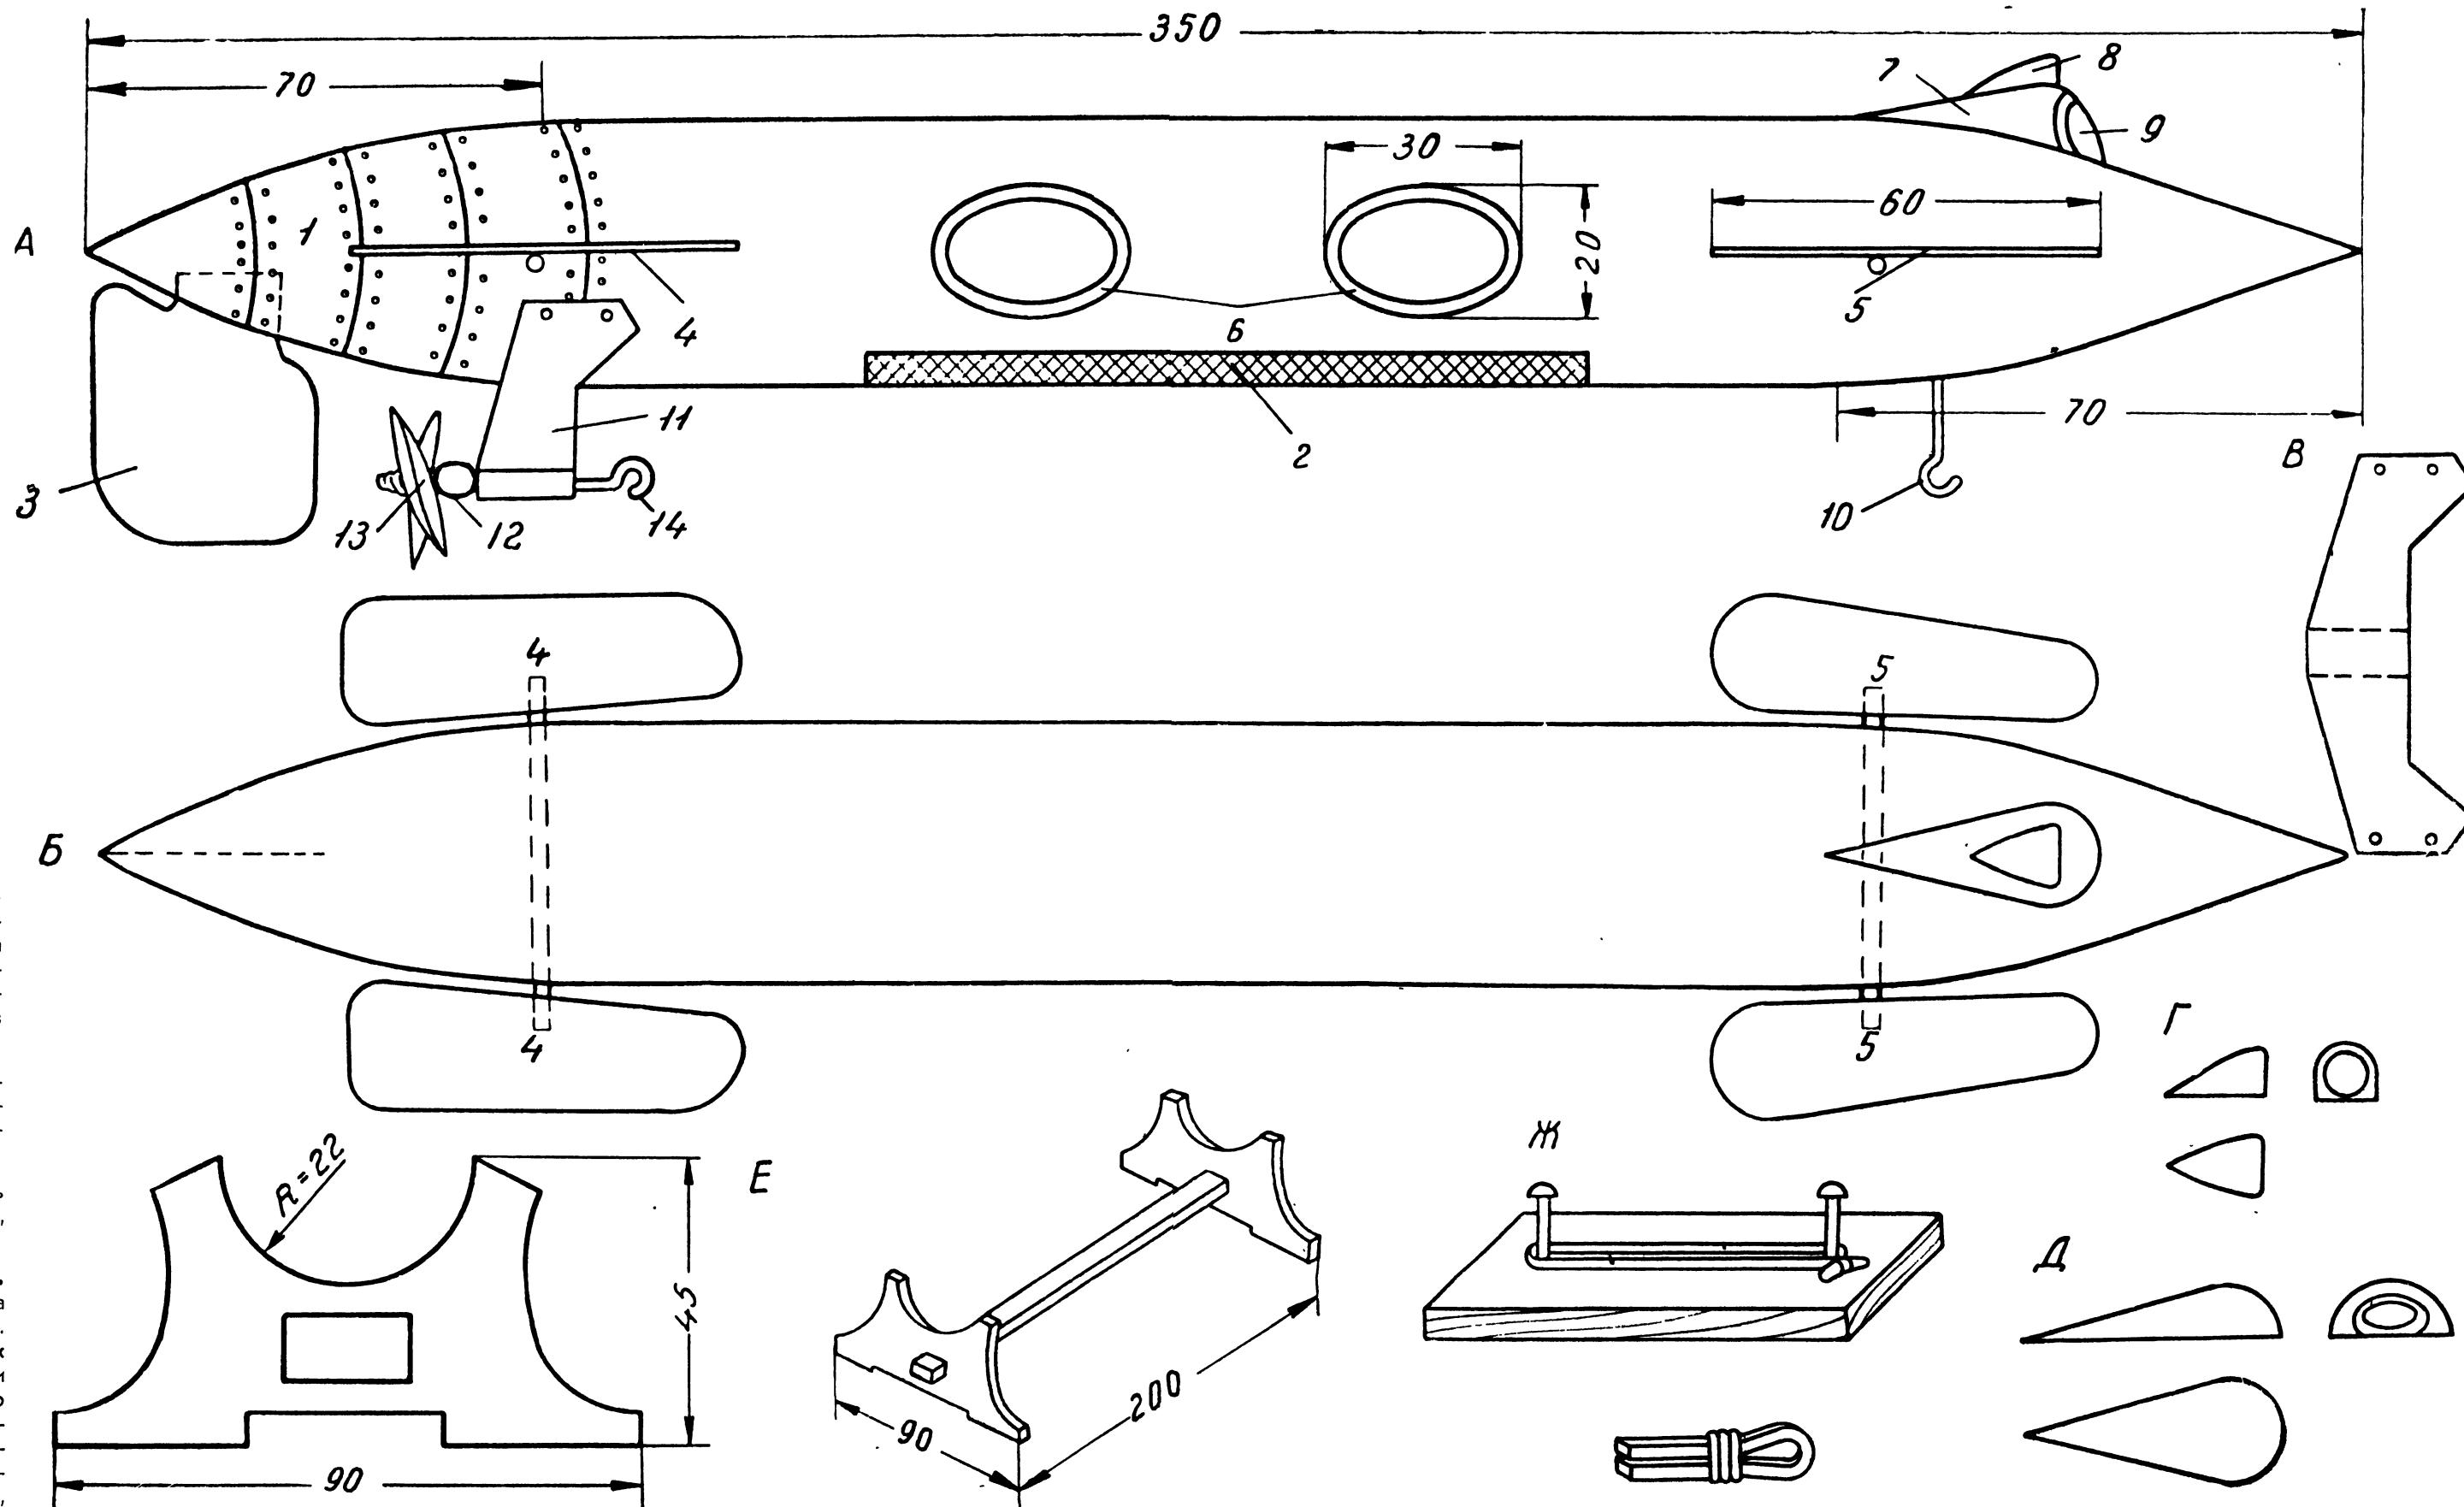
Модель подводного корабля «Наутилус» (в масштабе 1:200): А — вид сбоку; Б — вид сверху; В — выкройка кронштейна; Г — прожектор; Д — рубка; Е — подставка; Ж — заделка концов резинового двигателя.
